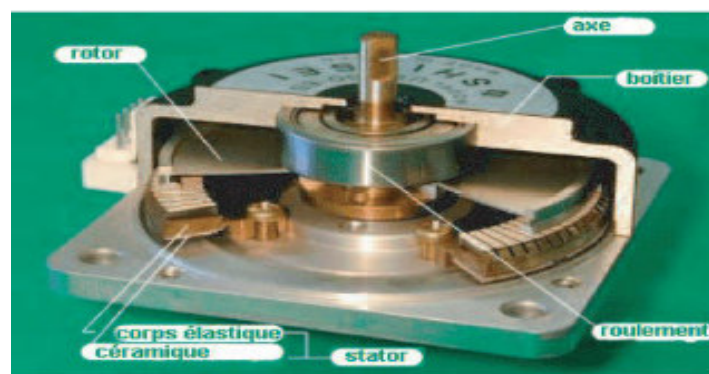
Vue éclatée du moteur SHINSEI USR60 [46].
